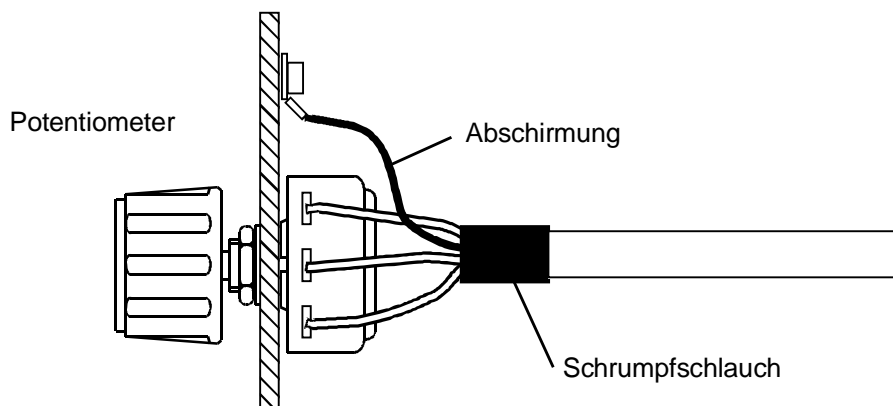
Beispiel einer Schirmbefestigung ohne Stecker
